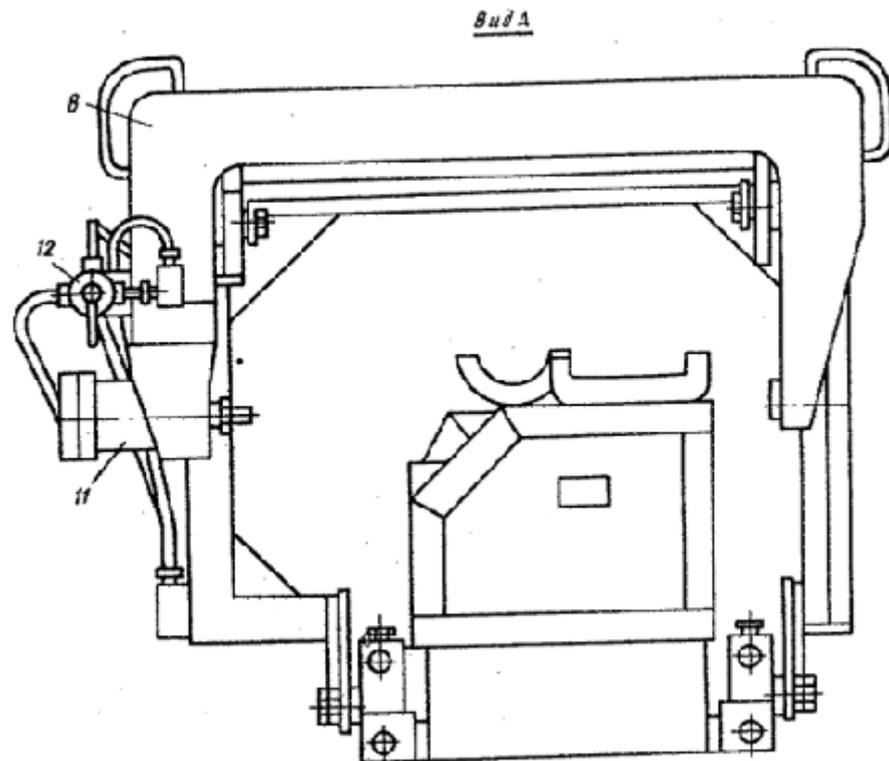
Вид А станда для разборки и сборки коробок передач
